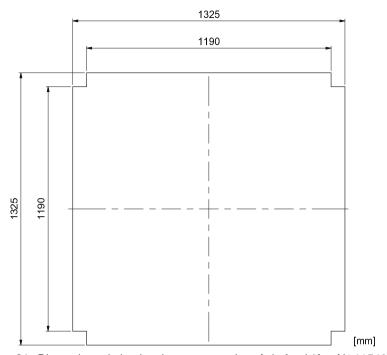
Dimensions de la planche en contreplaqué du fond (Art. N°11540)
